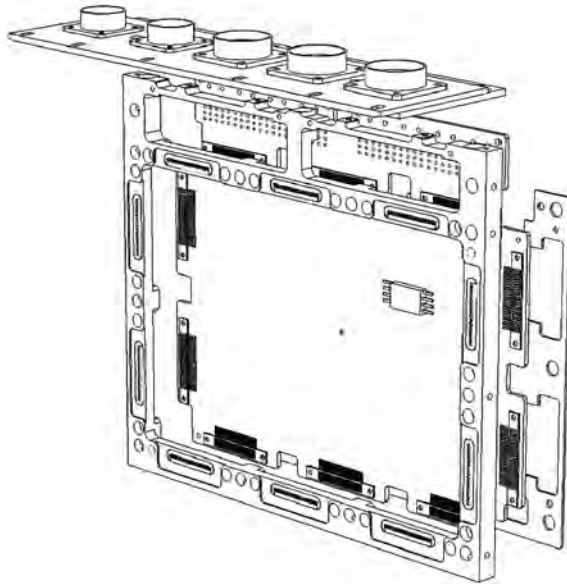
Схематичная сборка устройства с выходными соединителями
